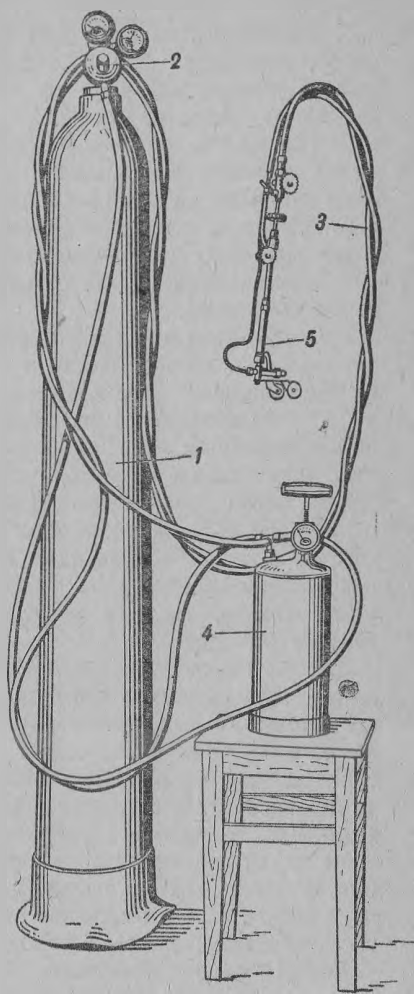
Бензосварочный аппарат с кислородным баллоном и резаком: 1 — кислородный баллон; 2 — редуктор; 3 — резиновый шланг; 4 — бак для бензина, бензола; 5 — горелка с головкой для резки.
